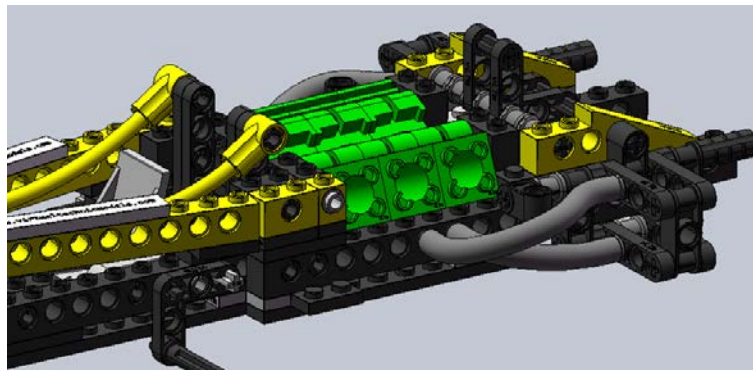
Componentes base del motor en 'V', dentro de la pieza chasis
